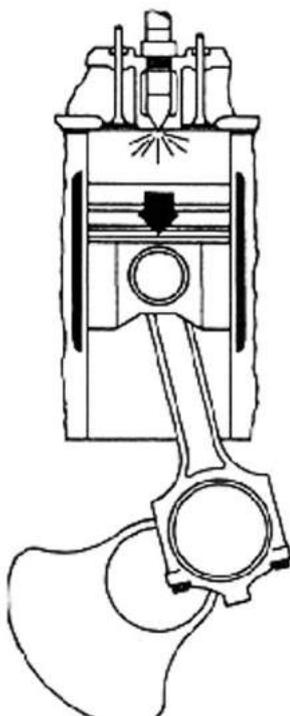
Pré-câmara de combustão (motor Diesel de injeção indirecta)
